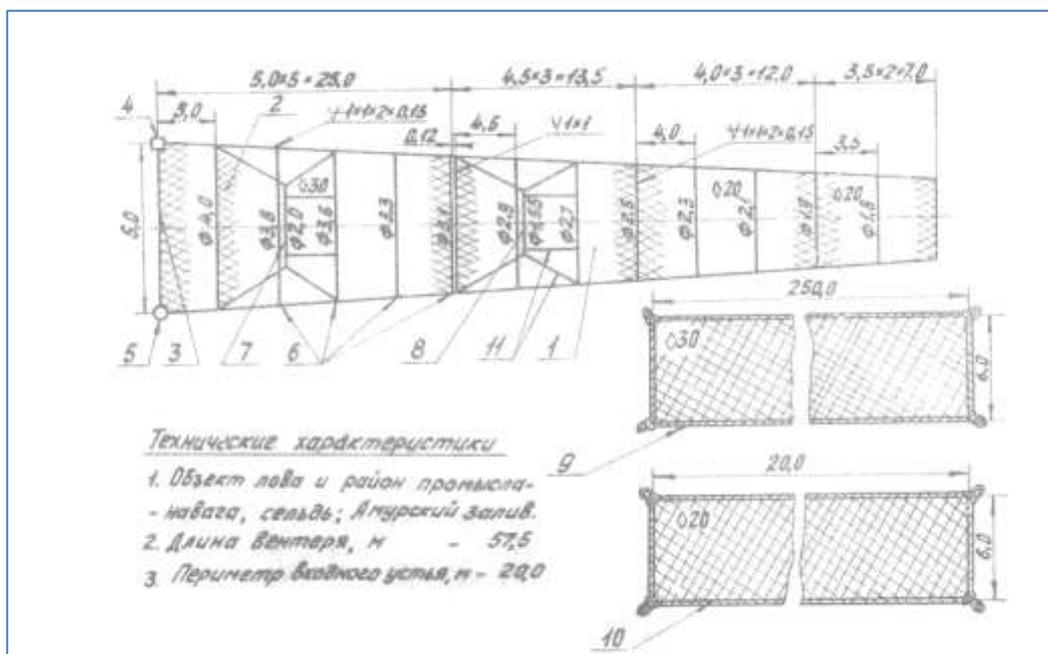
Сборочный чертёж вентера кательного 57,5х6 м
